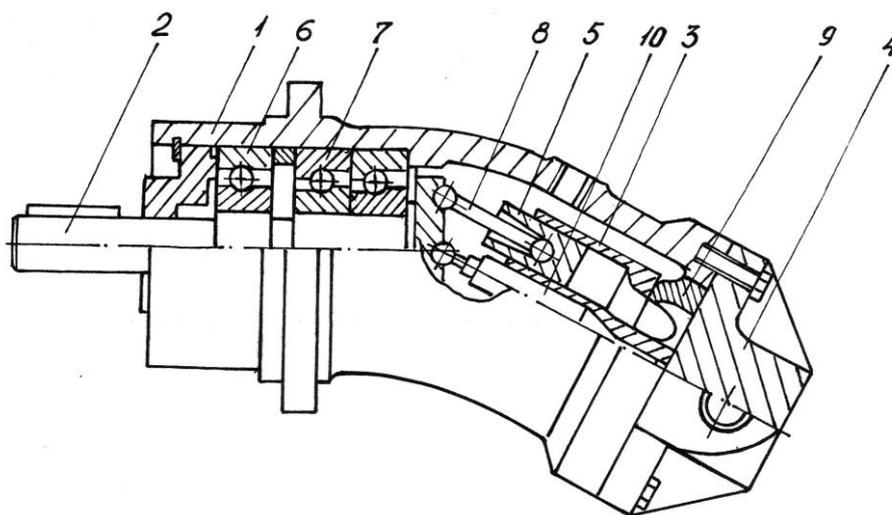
Аксиально-поршневой нерегулируемый насос-гидромотор типа 210: 1-корпус; 2-ведущий вал; 3-блок цилиндров; 4-крышка; 5-поршень; 6, 7-подшипники; 8-шатуны; 9- распределительный диск; 10-центральный шип
